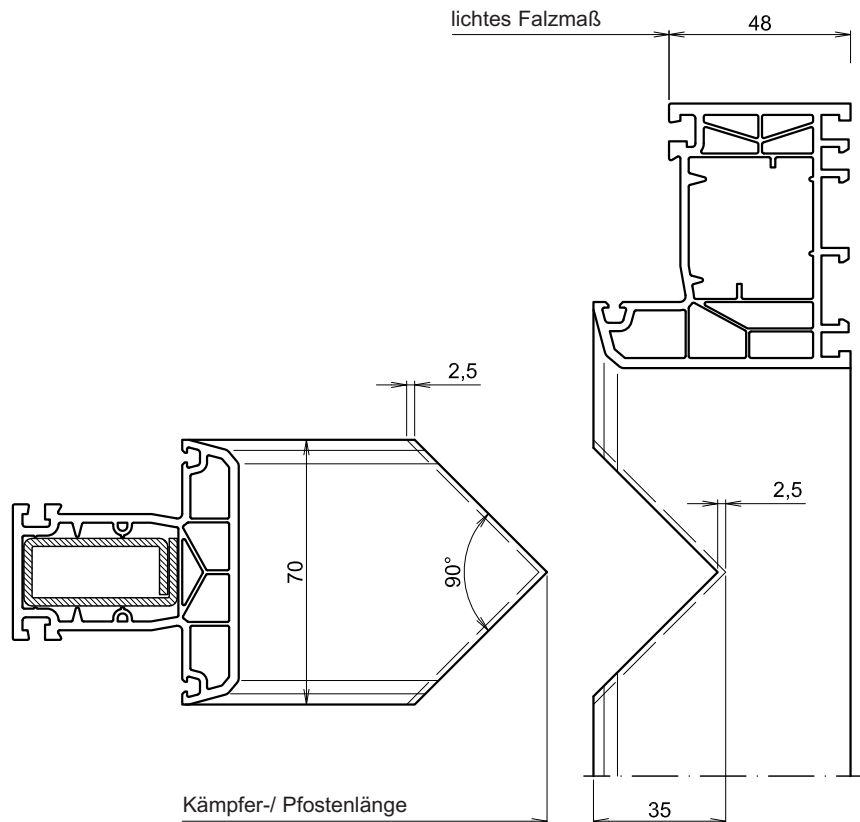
Einschweißmaße am Beispiel 63 01 00
